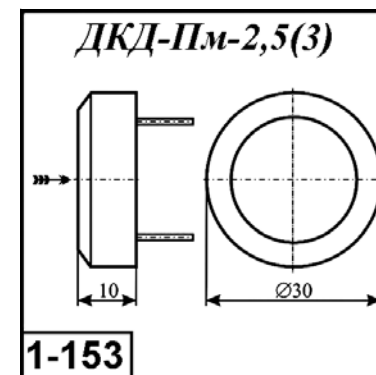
Внешний вид и габаритные размеры детектора ДКД-Пм-2,5-3.
